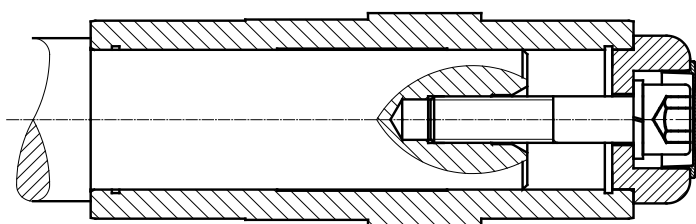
riduttore fissato ad un albero con spallamento mediante elemento di fissaggio
